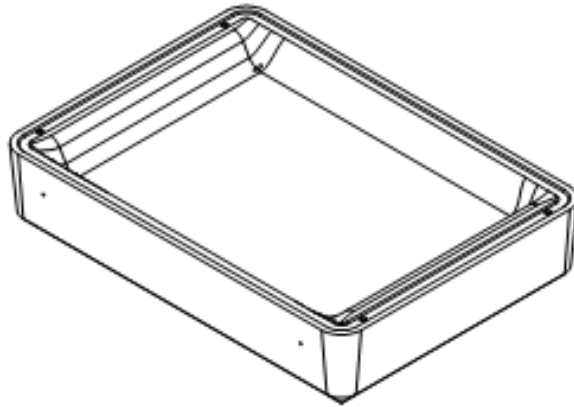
Матрица для формовки многослойных конструкций
